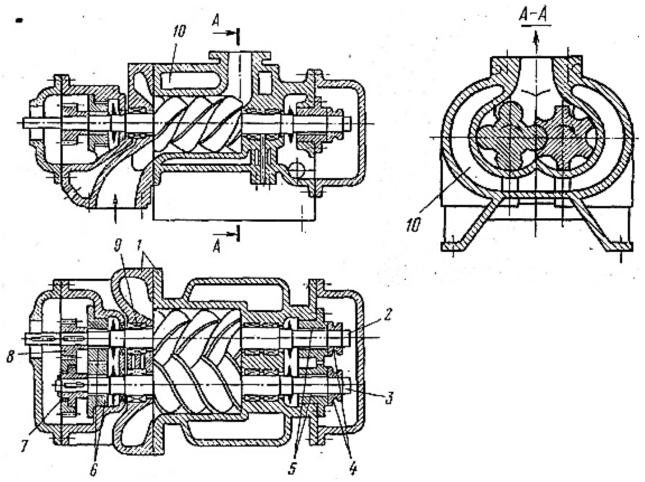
Винтовой компрессор с охлаждаемым корпусом: 1 – корпус, 2 – ведущий ротор, 3 – ведомый ротор, 4 – упорные подшипники, 5, 6 – опорные подшипники, 7, 8 – шестерни связи, 9 – уплотнения, 10 – полости для охлаждения
